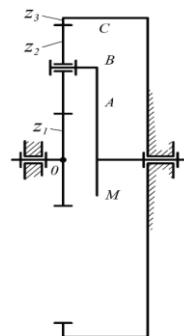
однорядный планетарный механизм с одновенцовыми сателлитами
